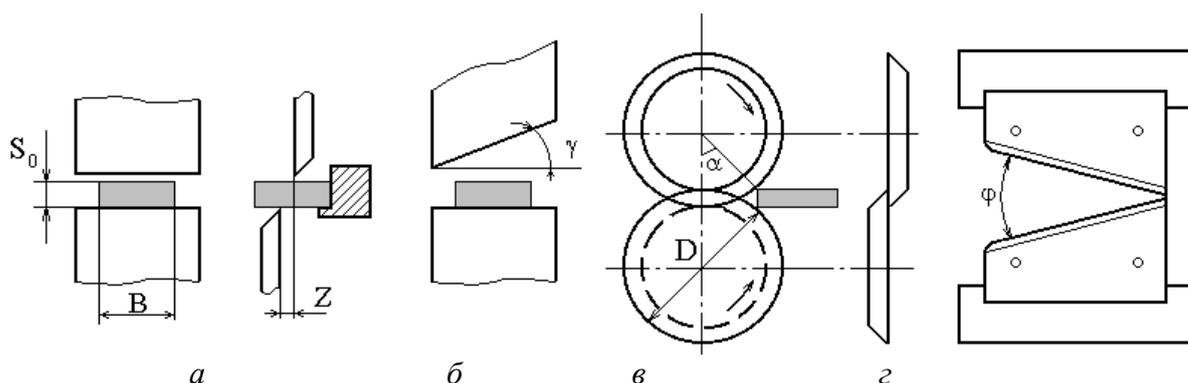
Схемы резки листового металла с помощью ножниц: а – ножницы с параллельными ножами; б – гильотинные ножницы; в – дисковые ножницы; г – вибрационные ножницы
